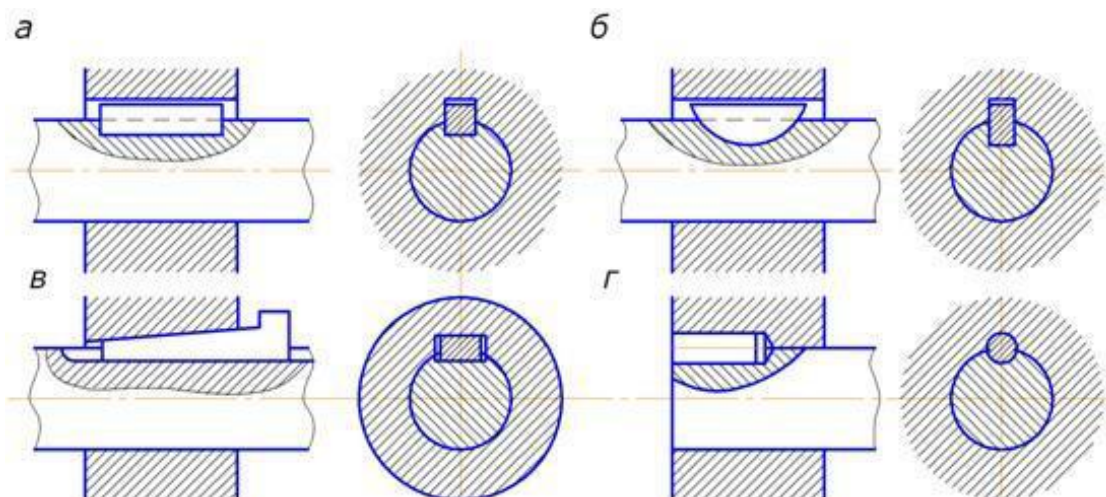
Види шпонок - а – призматична; б – сегментна; в – клинова; г – кругла
